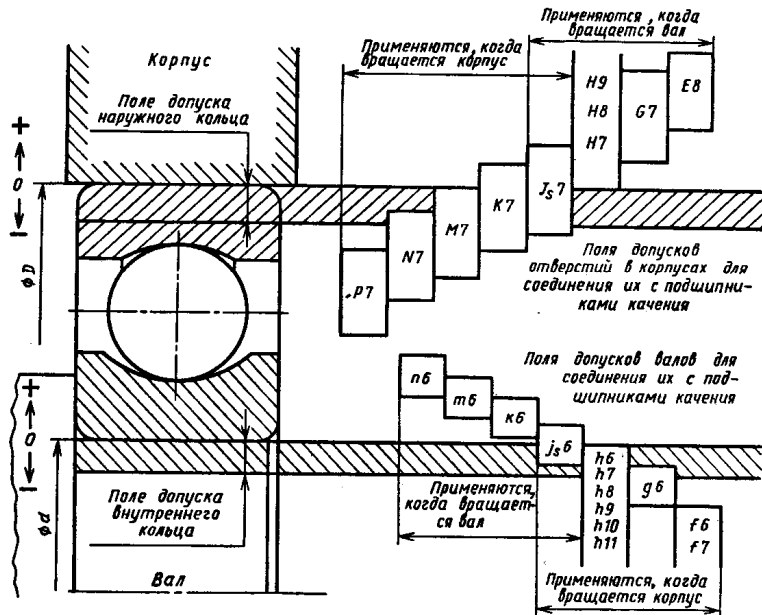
Схема расположения полей допусков на внутренний и внешний диаметры подшипников качения (на вал и корпус)
